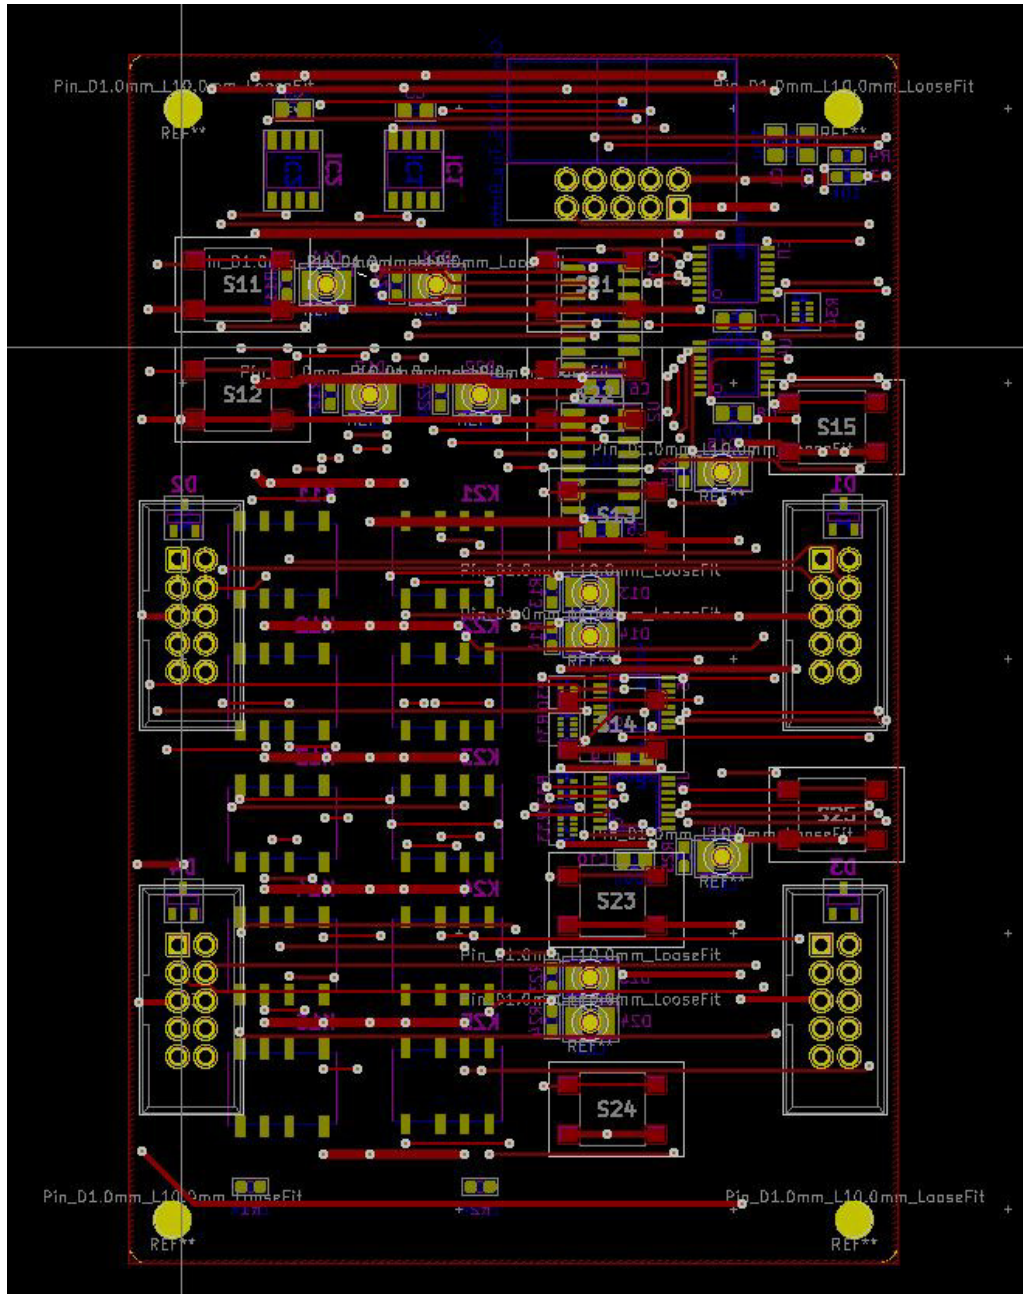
Failure Injection Board: Platinendesign Layer oben
